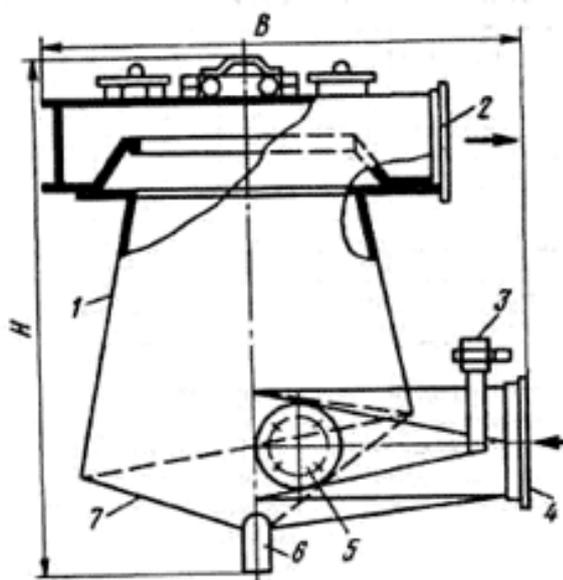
Циклон-промыватель СИОТ: 1 — корпус; 2 — патрубок для выхода воздуха; 3 — водоподводящая труба; 4 — патрубок для входа воздуха; 5 — смотровые люки; 6 — спусковой патрубок; 7 — коническая часть циклона.
